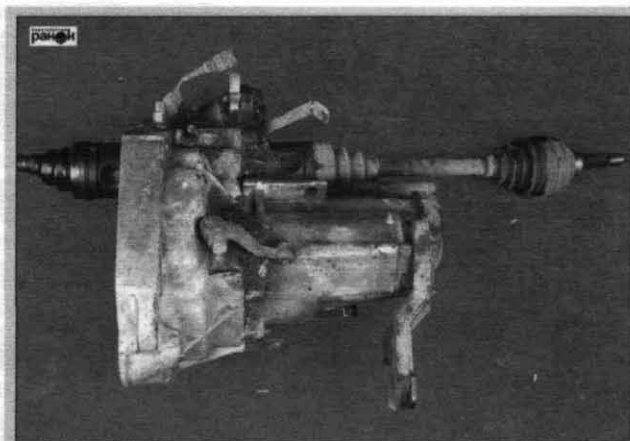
Коробка передач автомобиля «Sens» 1,3i в сборе с дифференциалом и приводами колес
